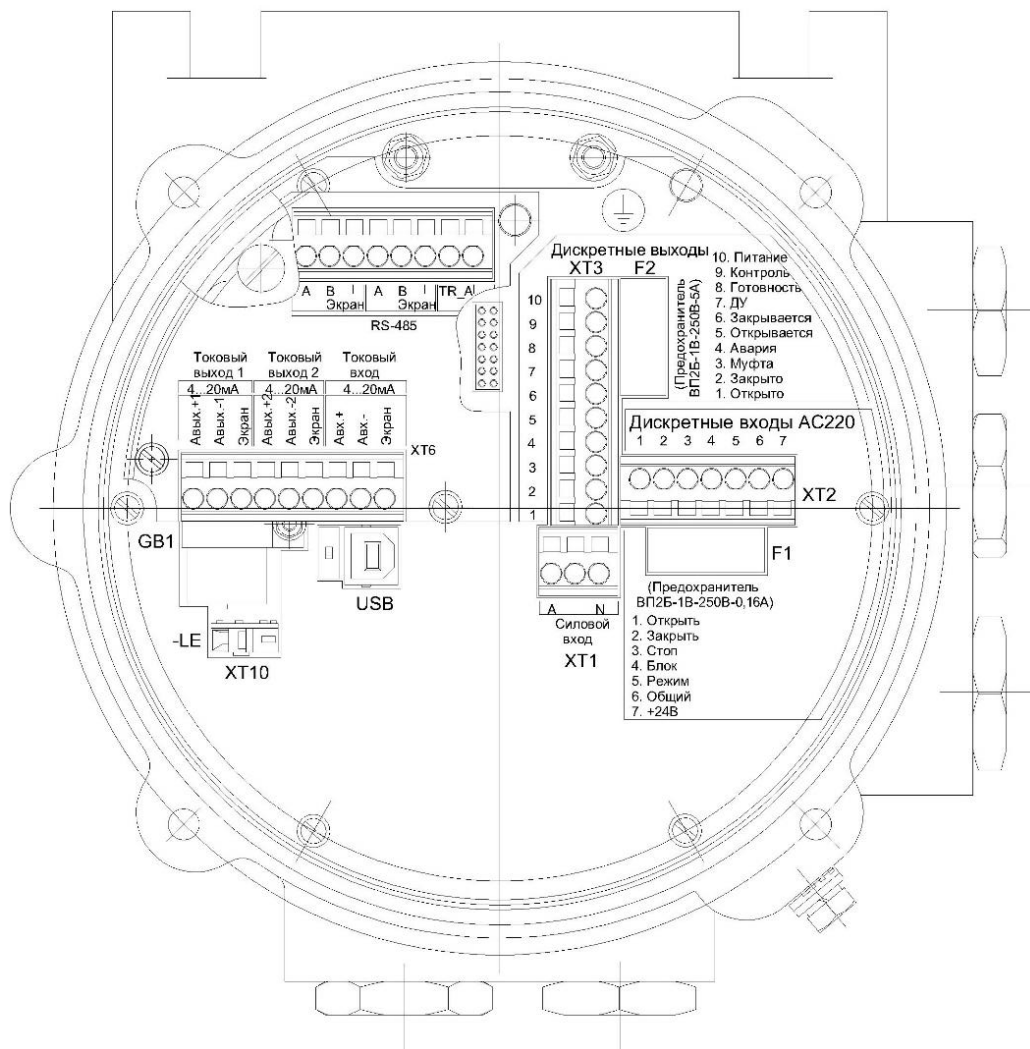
Типовой внешний вид бокса РэмТЭК конструктивного исполнения «80x0»
